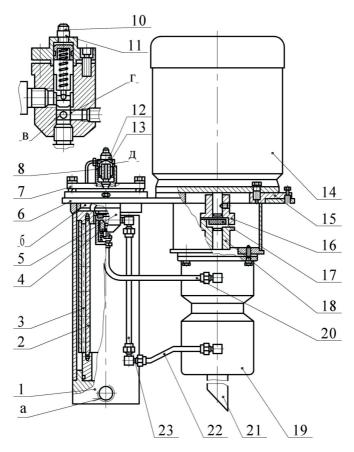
Установка очистного фильтра: 1 — фильтр; 2 — сетчатый фильтр; 3 — фильтрующая сетка; 4 — клапан; 5 — подпорный клапан; 6 — плита; 7 — крышка; 8 — пружина; 10 — винт; 11 — гайка; 12 — шток; 13 — указатель давления; 14 — электродвигатель; 15 — корпус; 16 — полумуфта; 17 — звездочка; 18 — полумуфта; 19 — пластинчатый насос; 20—23 — патрубки
